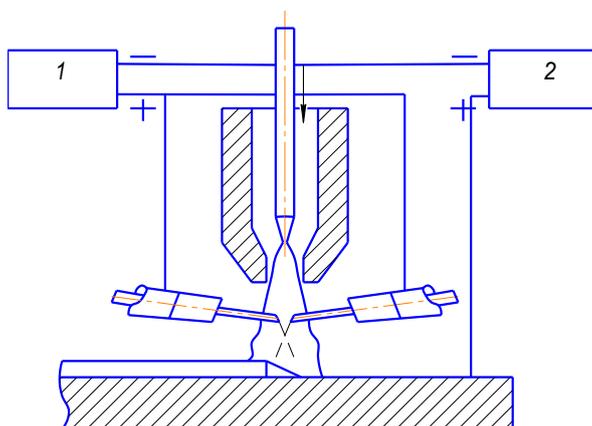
Схема плазменной наплавки с присадкой двух проволок:
